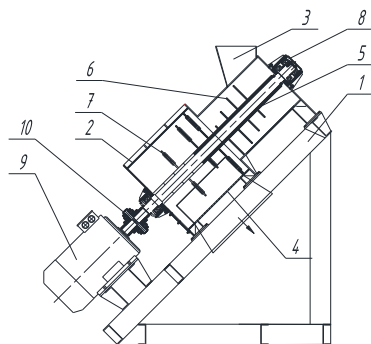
Молотковый измельчитель с наклонным корпусом: 1 – рама; 2 – корпус; 3,4 – камеры загрузки и выгрузки; 5 – рабочий орган; 6,7 – ударные элементы; 8 – подшипниковые опоры; 9 – электродвигатель; 10 – муфта
